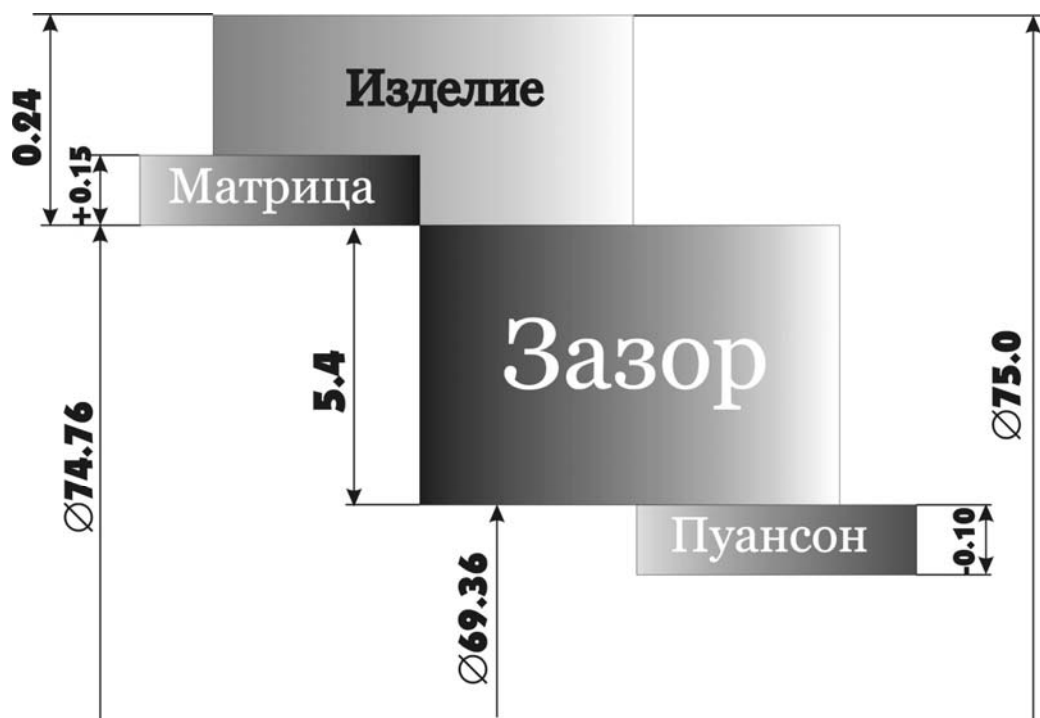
Схема расположения допусков на исполнительные размеры инструмента при отбортовке
